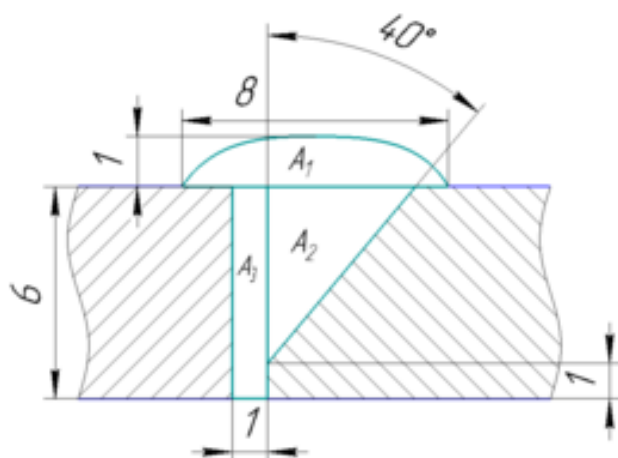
Схема сборки (а) и сварки (б) сварного шва для механизированной дуговой сваркой плавящимся электродом в среде защитных газах.
